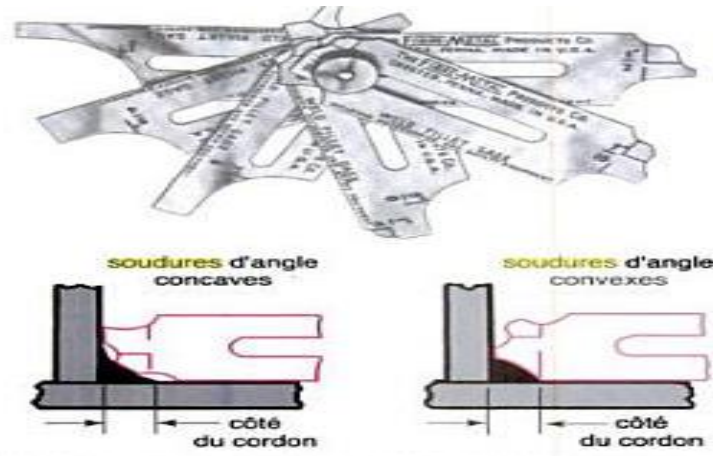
Calibres utilisés pour vérifier les soudures d'angles convexes ou concaves des soudures.[22]
